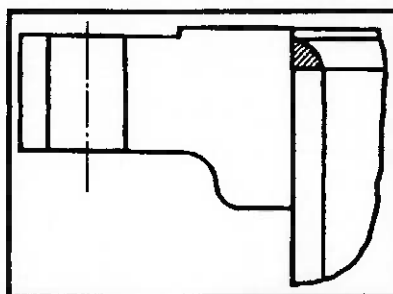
Posição de soldagem do filete externo do flange "Slip-On" ao pescoço da Boca de Visita
